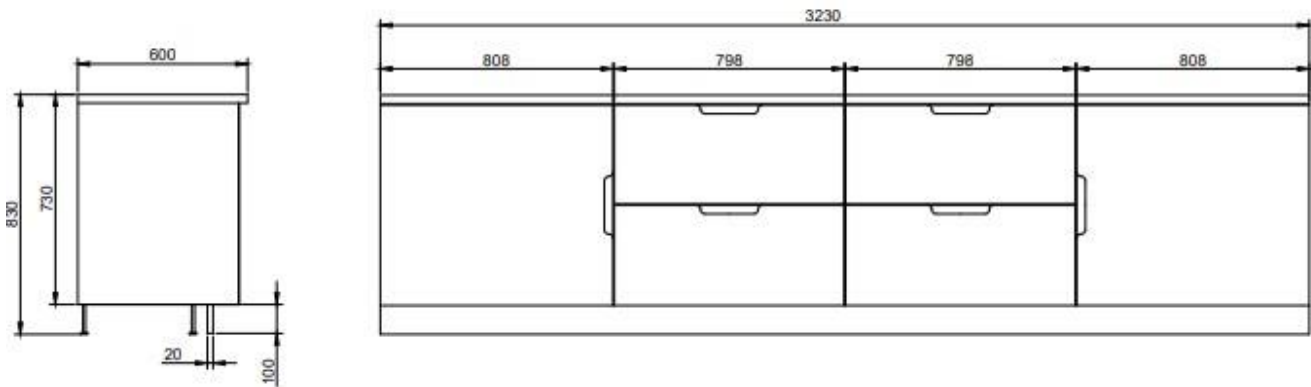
Equipamento Cerrado Matias, Desenho de Conjunto
